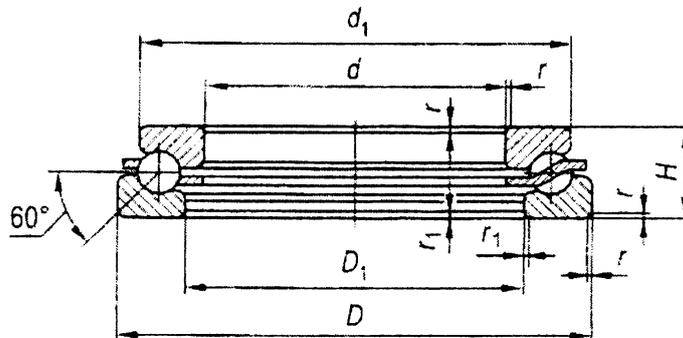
Подшипник шариковый упорно-радиальный одинарный исполнения 168000
